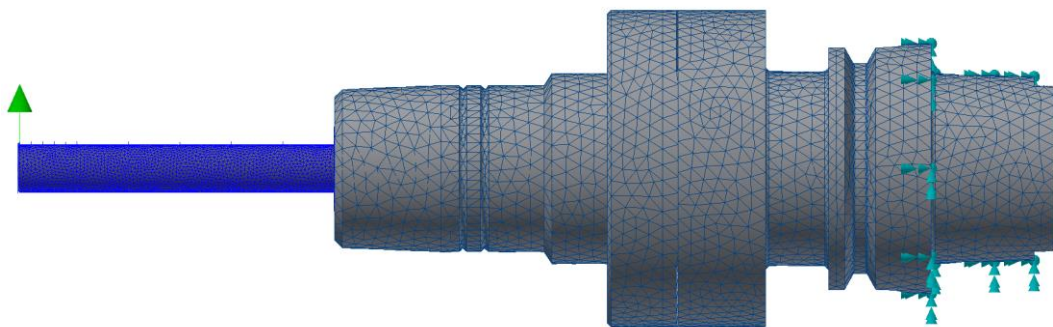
Zjednodušené CAD modely nástrojových systémů
